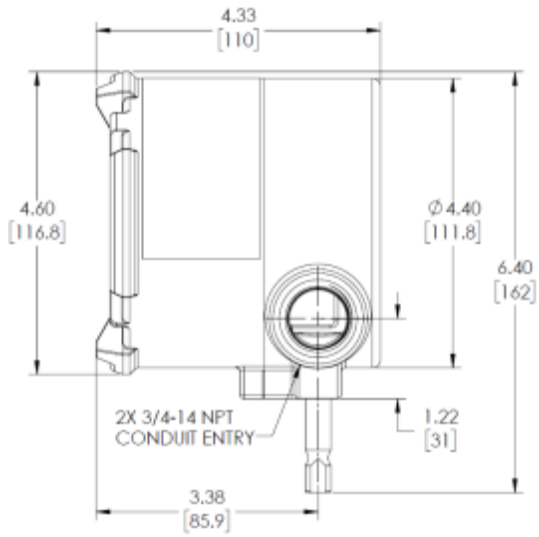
FL500 Umrisszeichnung, Seitenansicht
